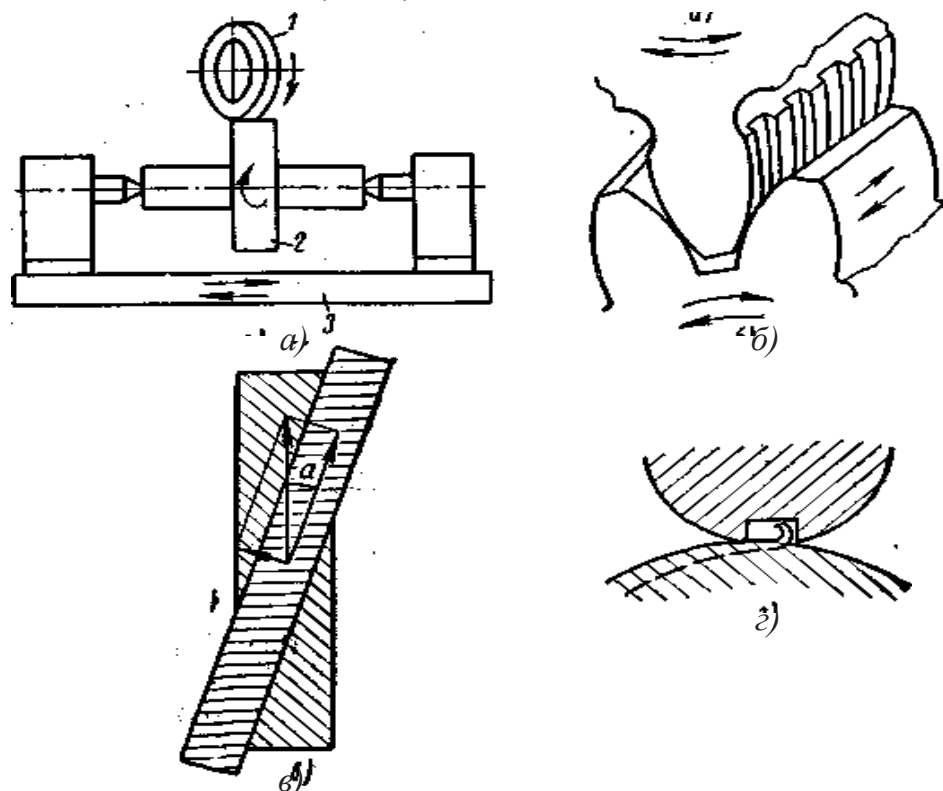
Отделка зубьев незакаленных зубчатых колес шевингованием: *a* – схема установки заготовки на столе станка; *б* – направление движения инструмента и заготовки; *в* – угол скрещивания осей заготовки и шевера; *г* – формирование стружки
